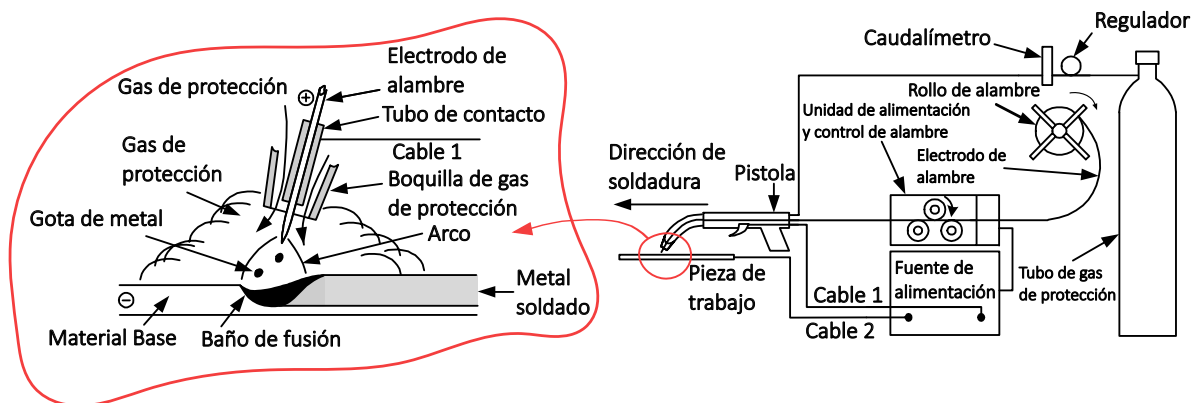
Soldadura por Arco Metálico con Gas (GMAW) [16].
